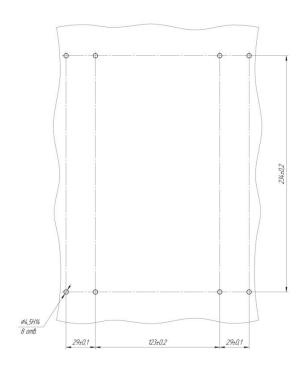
Габаритные и присоединительные размеры устройства РС830-ДТ2 при внешнем монтаже, обеспечивающем его поворот вверх/вниз
